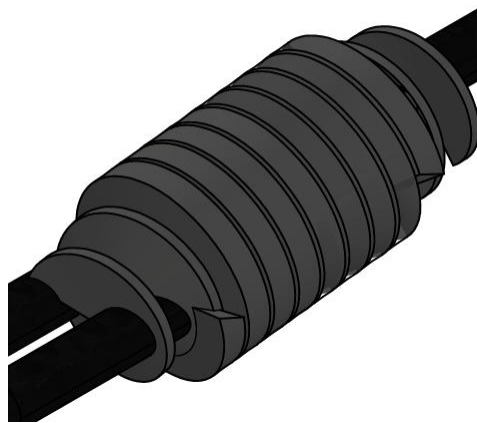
Aplicación de cinta autofundente de media tensión.
